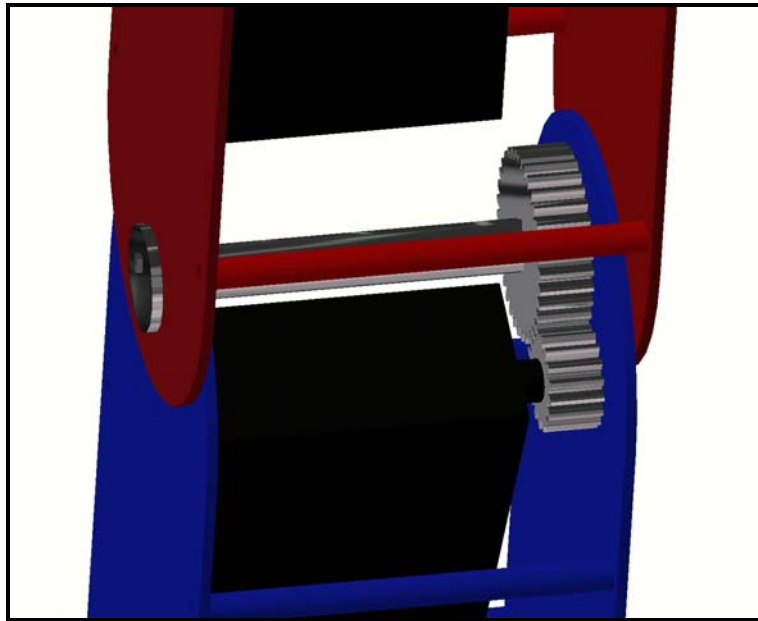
Junta rotacional da perna esquerda, vista de trás.
